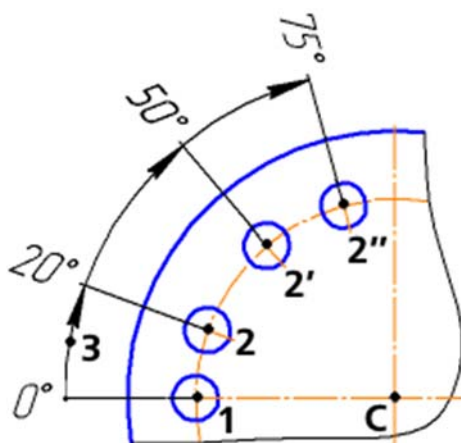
Простановка угловых размеров с общей размерной линией (способ задания сторон углов – по трем точкам)
